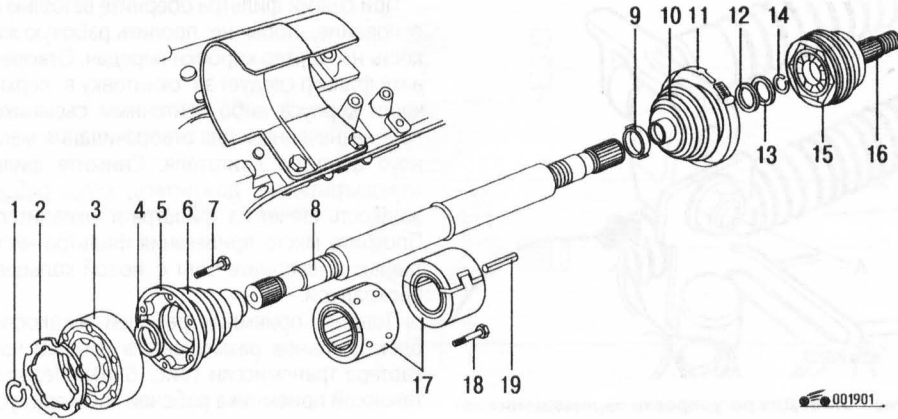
Привод переднего колеса: 1 – стопорное кольцо; 2 – специальная прокладка; 3 – внутренний шарнир; 4, 13 – шайбы; 5, 6, 10 – защитные чехлы; 7, 18 – болты; 8 – приводной вал; 9 – малый хомут; 11 – большой хомут; 12 – тарельчатая шайба; 14 – стопорное кольцо; 15 – наружный шарнир; 16 – хвостовик наружного шарнира; 17 – гаситель крутильных колебаний (из двух частей); 19 – штифт
